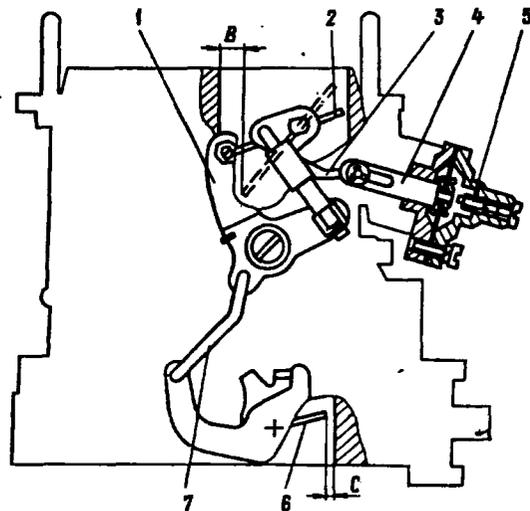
Регулировка привода пускового устройства карбюратора 2107-1107010: 1 - трехплечий рычаг управления воздушной заслонкой; 2 - воздушная заслонка; 3 - тяга пускового устройства; 4 - шток; 5 - регулировочный винт; 6 - дроссельная заслонка первой камеры; 7 - тяга привода дроссельной заслонки
